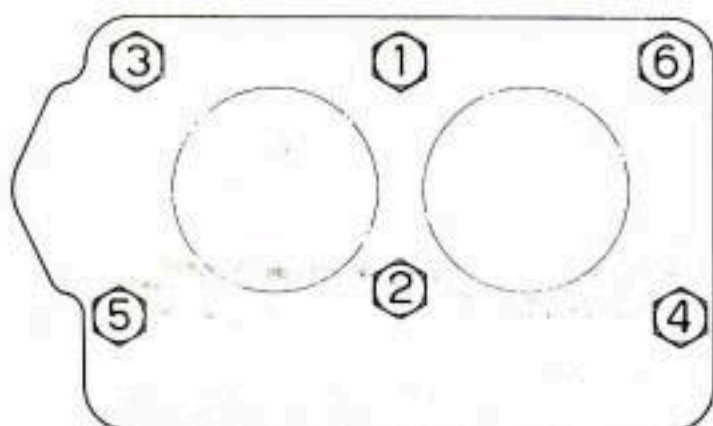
Rimontaggio del motore: schema dell'ordine di serraggio delle viti di fissaggio testa cilindri.
